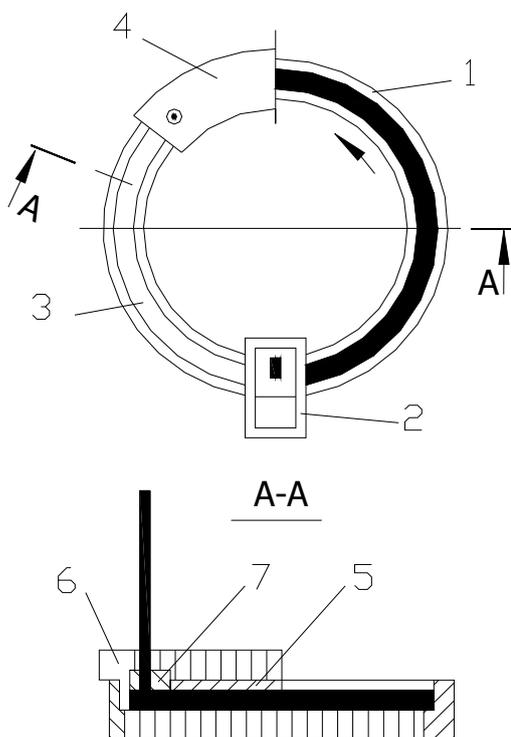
Схема установки непрерывного литья и прессования: 1 – рабочее колесо (кристаллизатор); 2 – литниковая коробка; 3 – кольцевая канавка; 4 – неподвижная часть контейнера («башмак»); 5 – дугообразный выступ «башмака»; 6 – упор «башмака»; 7 – матрица для прессования
